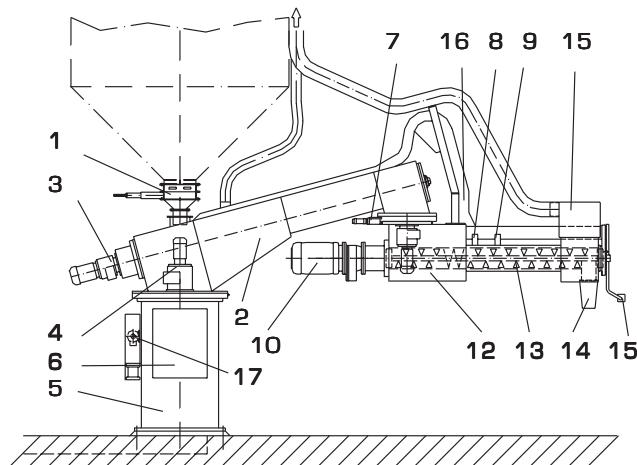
Устройство смесителя: 1 – дозатор для подачи двух наполнителей в требуемой пропорции; 2 – транспортный шнек; 3 – привод транспортного шнека; 4 – привод поворота рукоава; 5 – основание смесителя; 6 – технический шкаф; 7 – тормоз; 8 – дозатор отвердителя; 9 – дозатор смолы; 10 – привод смесителя; 11 – смеситель; 12 – камера финишной очистки песка; 13 – табло управления; 14 – выпускная воронка смесителя; 15 – вытяжка у головки смесителя; 16 – вытяжка камеры кипящего слоя; 17 – насосные устройства
